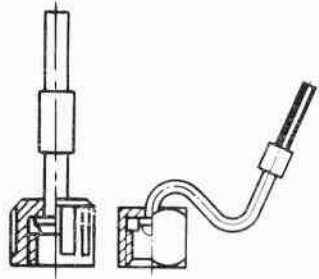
Приспособление для проверки угла опережения подачи топлива
